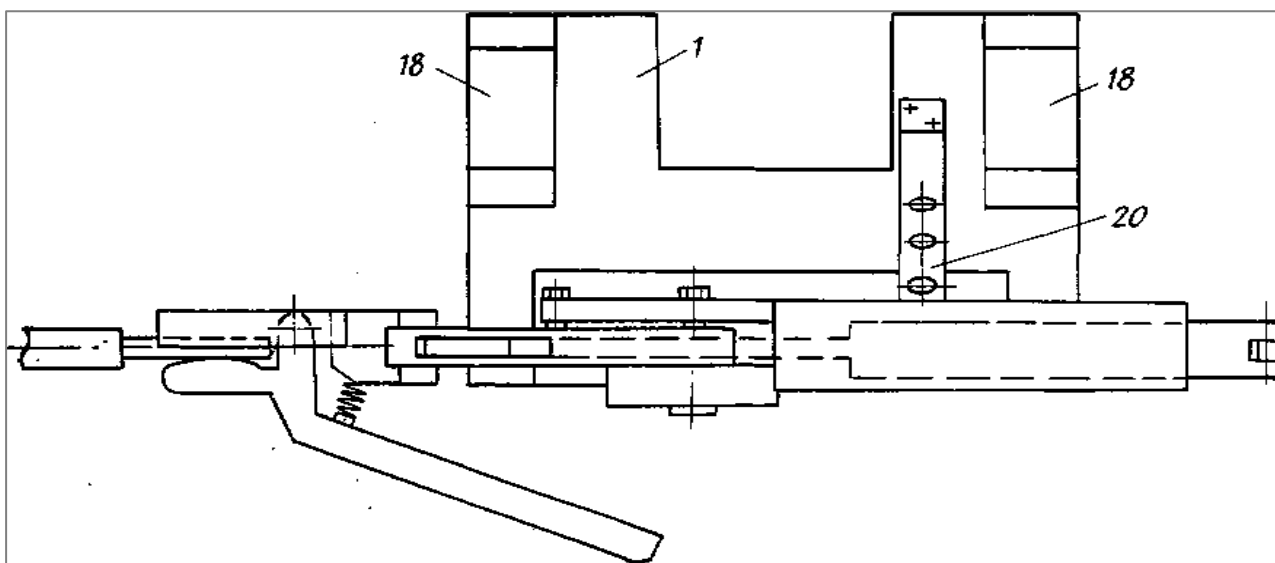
б – Устройство для сварки наклонным электродом вид сверху
